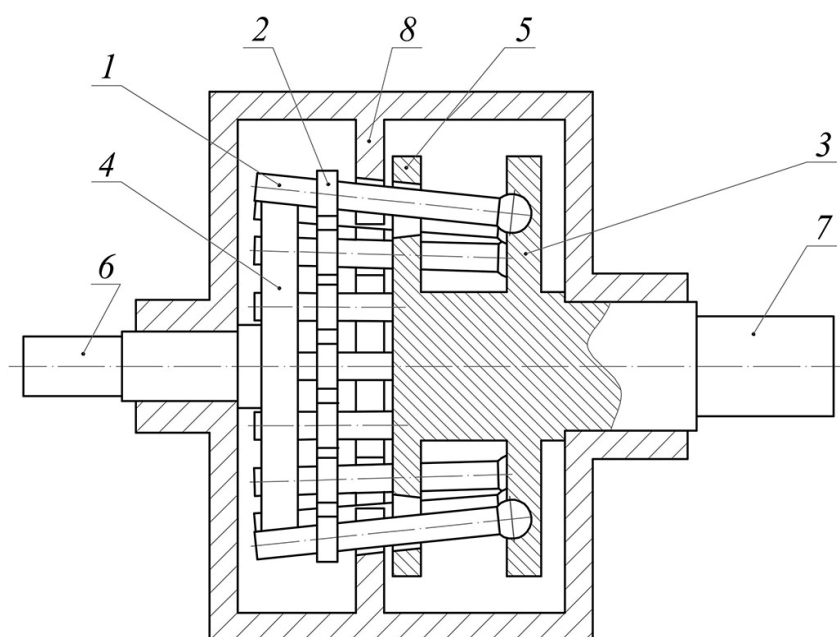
Волновая передача с гибким звеном в виде пальцевой цепи: 1 – палец, 2 – пластина, 3 – опорный диск, 4 – генератор, 5 – направляющий диск, 6 – входной вал, 7 – выходной вал, 8 – жесткое колесо
